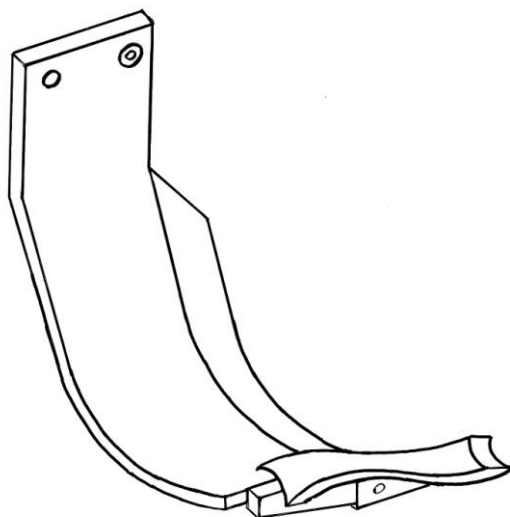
Рабочий орган чизельного плуга-рыхлителя типа ПРН
